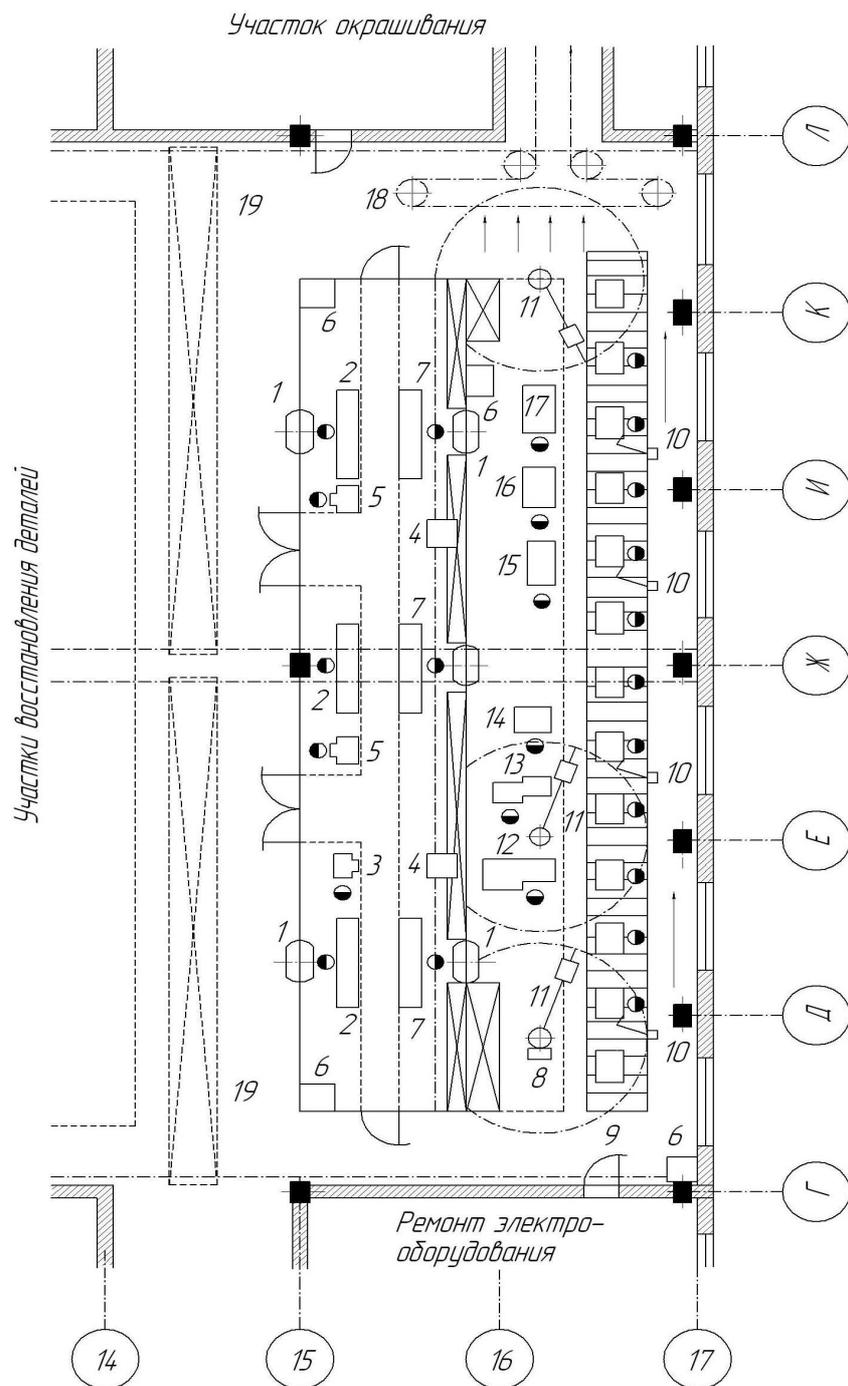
Планировка комплектовочно-сборочного участка: 1 – поворотный стеллаж; 2 – сортировочный стол; 3 – стенд для разборки шатунов и толкателей; 4 – опорный кран-штабелер; 5 – стенд для пневмоконтроля; 6 – пожарный пост; 7 – комплектовочный стол; 8 – стенд для узловой сборки сальникодержателя; 9 – конвейер для общей сборки; 10 – консольный гайковерт; 11 – консольно-поворотный кран ( $q = 160$  кгс); 12 – станок балансировочный МС-9716; 13 – стенд для сборки коленчатого вала с маховиком и сцеплением; 14 – стенд для сборки распределительного вала с шестерней, противовесом и пластиной; 15 – стенд для теплопрессовой сборки шатунно-поршневой группы; 16 – машина для погружной очистки шатунно-поршневых групп; 17 – стенд для сборки головки цилиндров; 18 – подвесной конвейер; 19 – кран-балка ( $q = 2$  тс)
